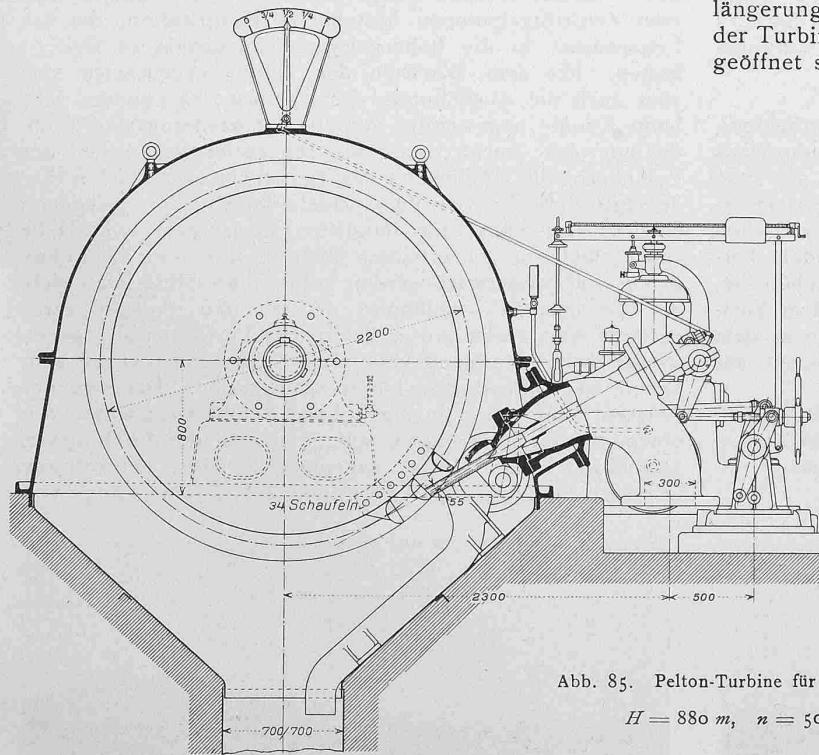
Pelton-Turbine für Vouvry. — Ateliers de Constr. Mécaniques de Vevey.
